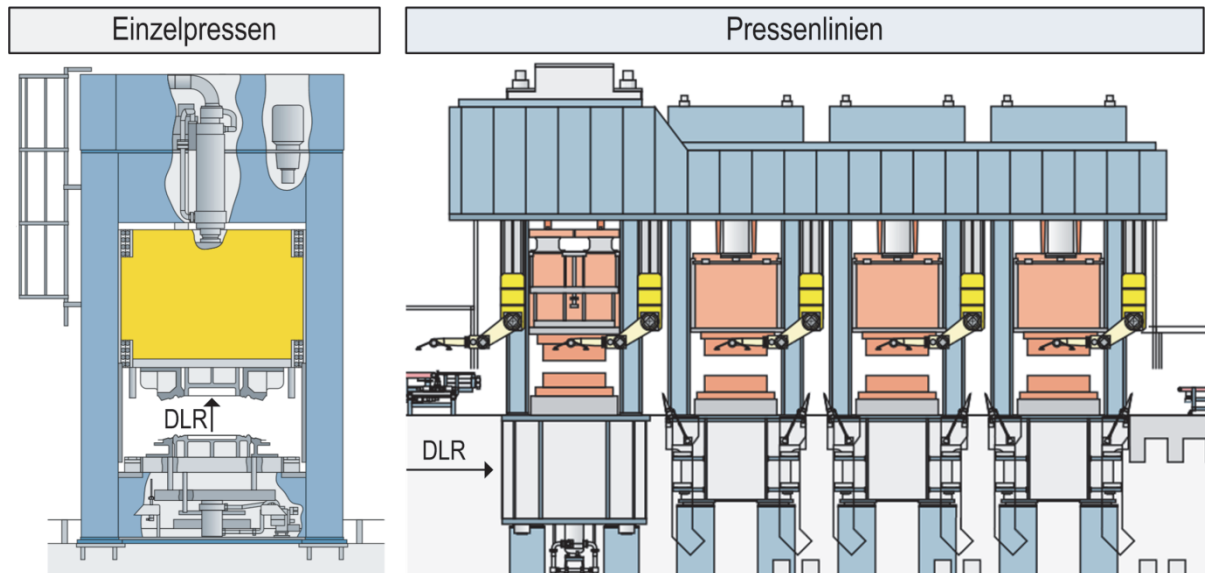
Pressmaschinen für Einzelwerkzeuge (in Anlehnung an SCHULER [91])
